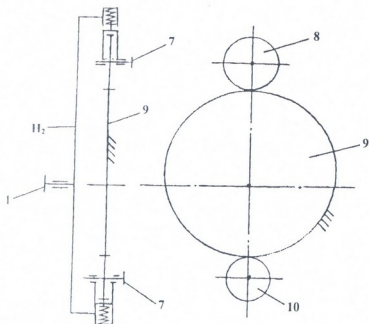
Двухступенчатая планетарная передача эксцентричным колесом
